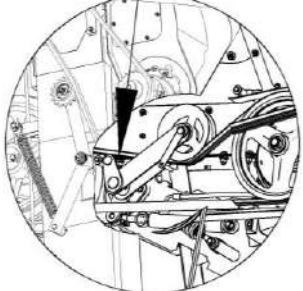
Схема смазки комбайна (вид справа)
